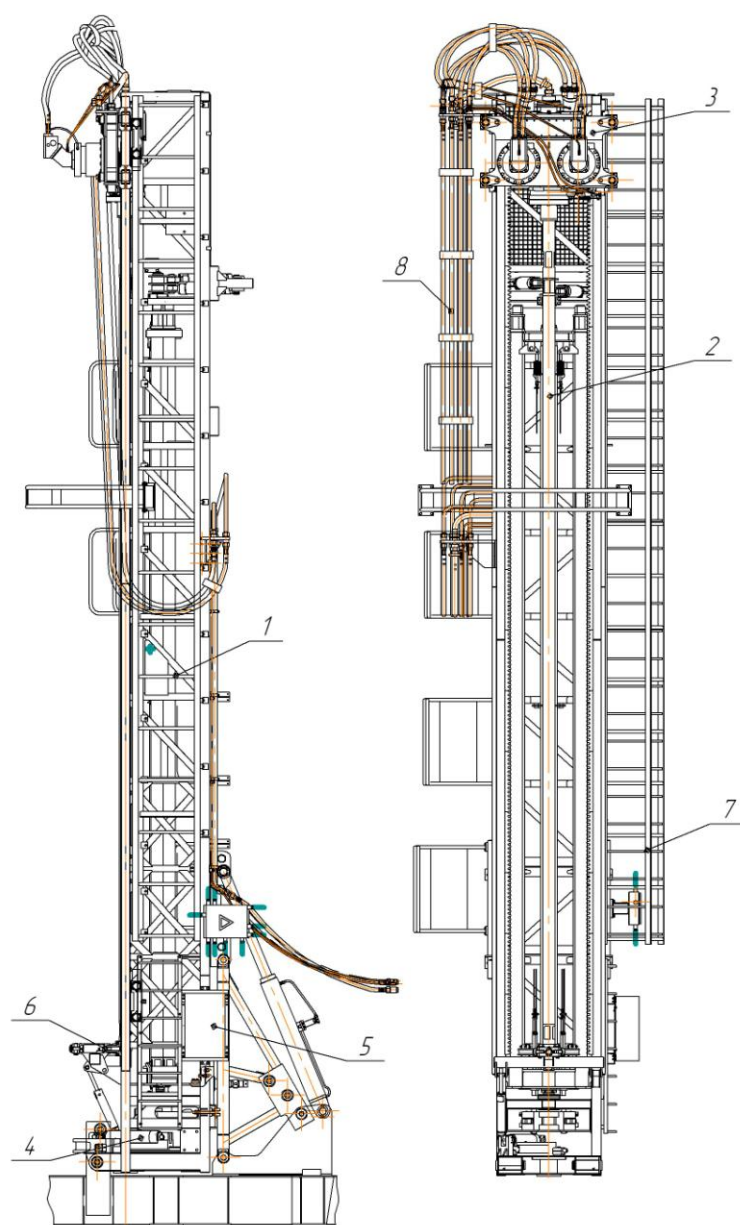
Мачта станка СБШ 160/200-40: 1 – каркас мачты; 2 – сепаратор; 3 – вращательно-подающий механизм; 4 – устройство для разбива бурового става; 5 – гидроблок; 6 – люнет; 7 – лестница; 8 – гирлянда
